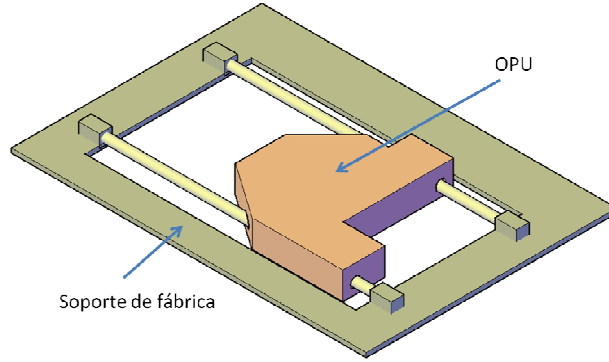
Montaje de la OPU en el soporte de fábrica
